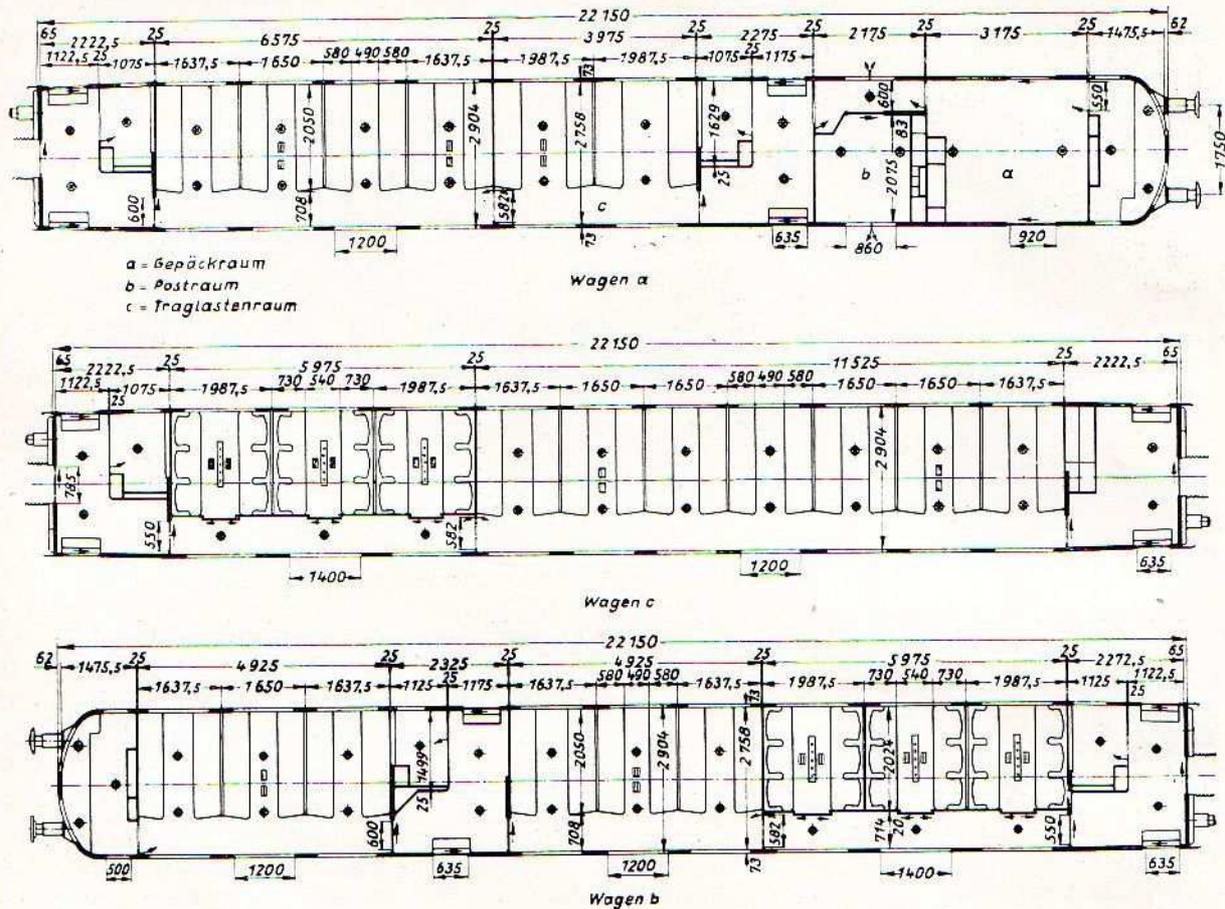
Grundriß des dreiteiligen Wechselstromtriebwagen.
